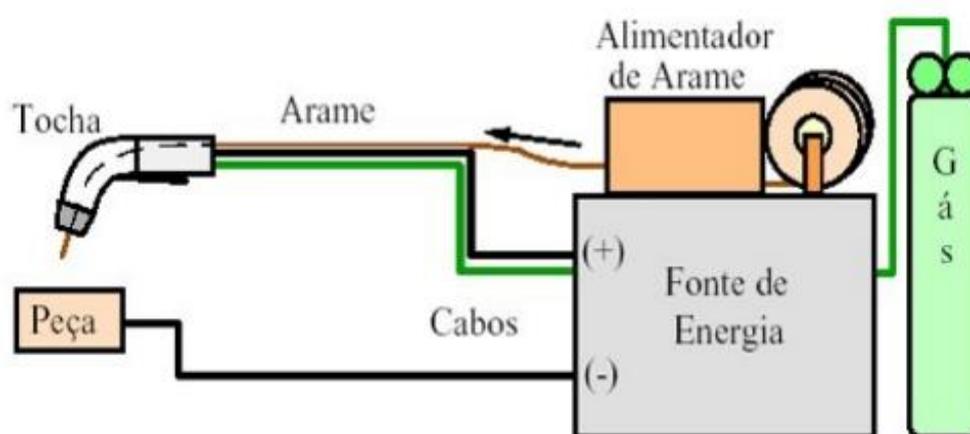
Máquina de soldadura MIG/ MAG
